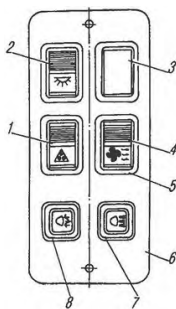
Панель выключателей автомобилей Урал-55571-40: 1 – выключатель фонарей знака автопоезда; 2 – выключатель плафона кабины; 3 – заглушка; 4 – переключатель отопителя кабины; 5 – рамка выключателей; 6 – панель щитка выключателей; 7 – выключатель фары освещения разгрузочной площадки; 8 – выключатель света задней противотуманной фары
